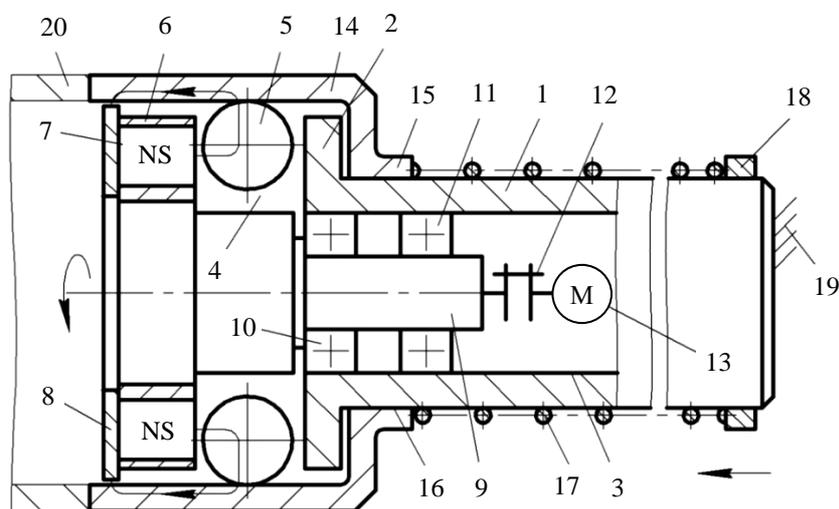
Конструкция инструмента для СМДН с цилиндрической кольцевой камерой и защитным кожухом
